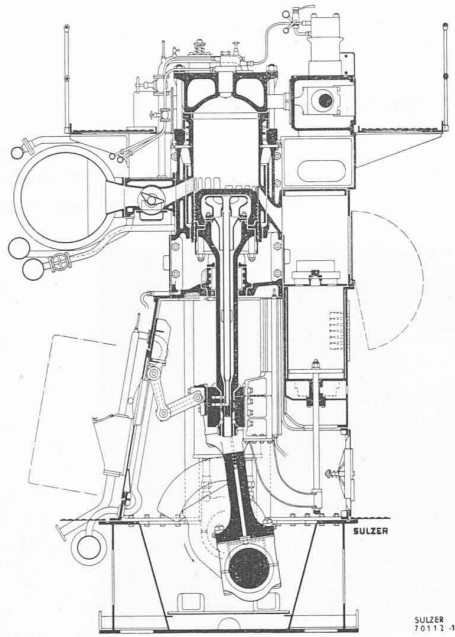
Coupe transversale schématique du nouveau moteur «RS58» en exécution soudée. On remarquera le presse-étoupe séparant le cylindre du carter, la faible hauteur du piston et le tiroir oscillant monté sur la conduite d'échappement.
